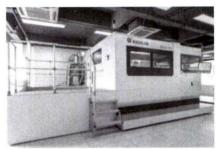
工业级喷墨砂型 3D 打印机 Fig.9 Industrial grade ink-jet sand 3D printer
